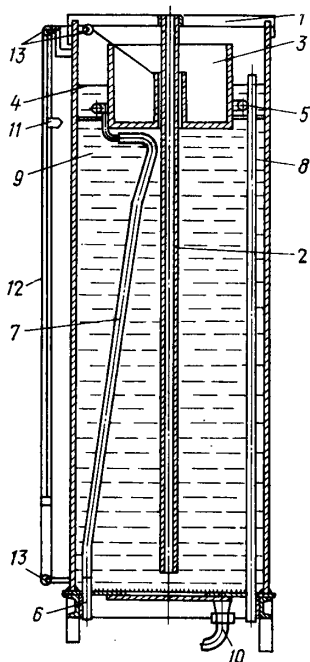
Схема отпуска резервуара передвигающимся источником нагрева:
